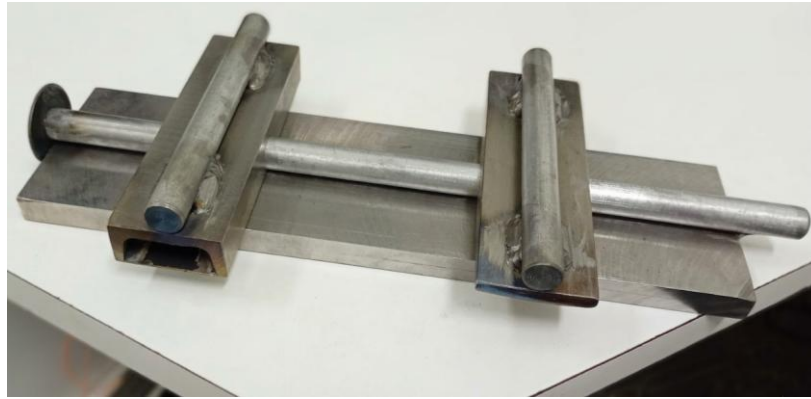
Dispositivo de apoyo para ensayo de flexión (IRAM 11656)
